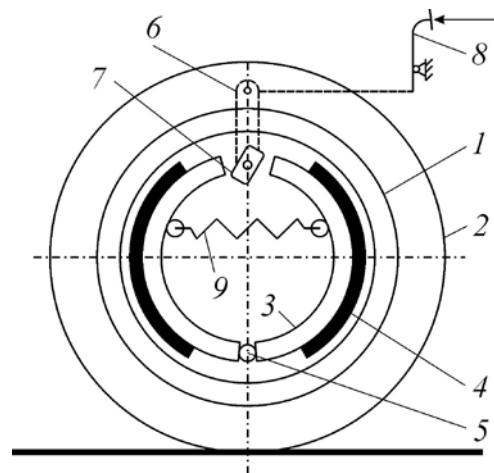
Схема колодочного тормоза: 1 – тормозной барабан; 2 – колесо автомобиля; 3 – тормозные колодки; 4 – фрикционные накладки; 5 – ось опоры колодок; 6 – рычаг поворота; 7 – поворотный кулак; 8 – тормозная педаль; 9 – возвратная пружина
